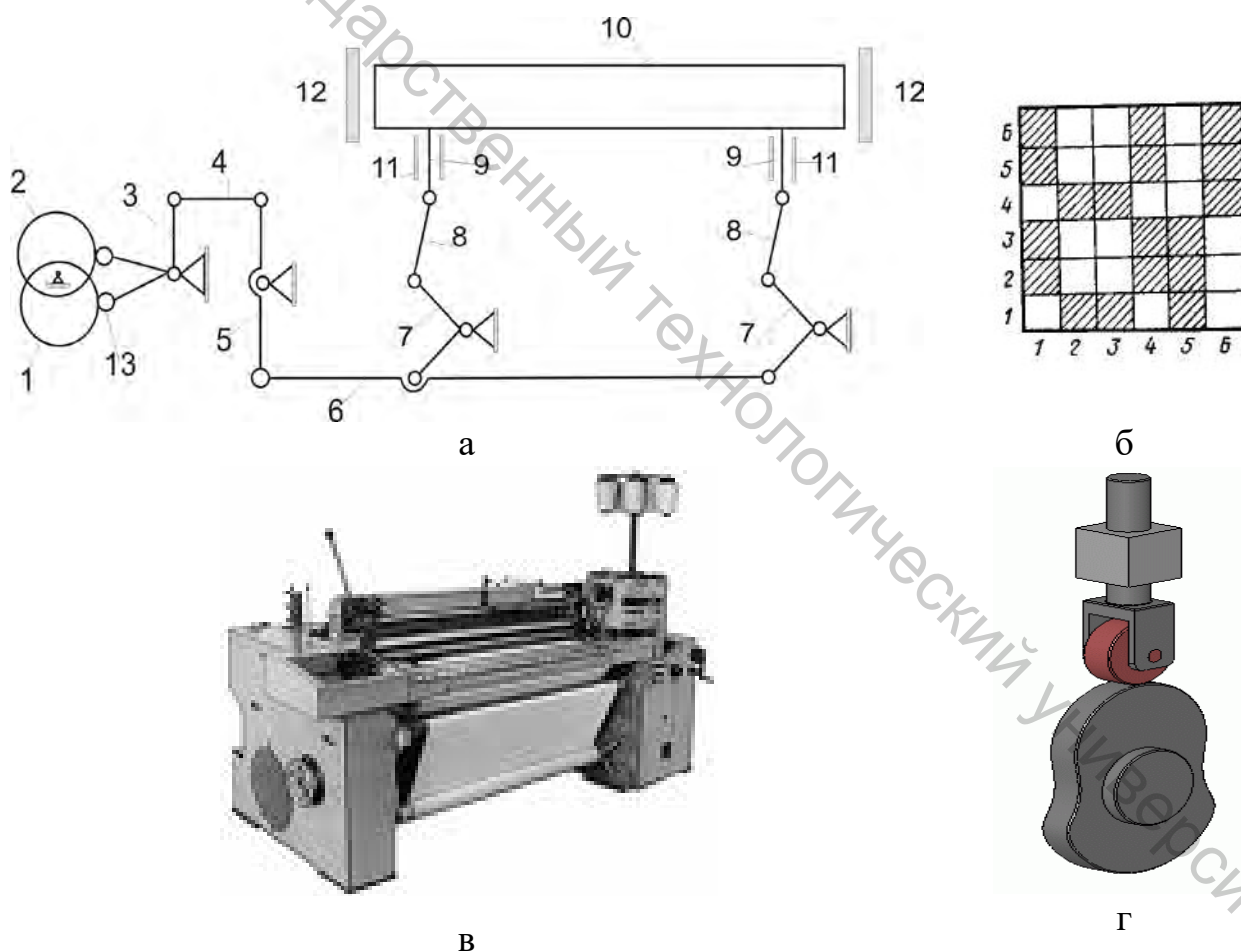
Схема кулачкового зевобразовательного механизма станка СТБ (а); рисунок переплетения для подбора кулачков (б), внешний вид ткацкого станка СТБ с кулачковым зевобразовательным механизмом (в), кулачок с роликом (г)
